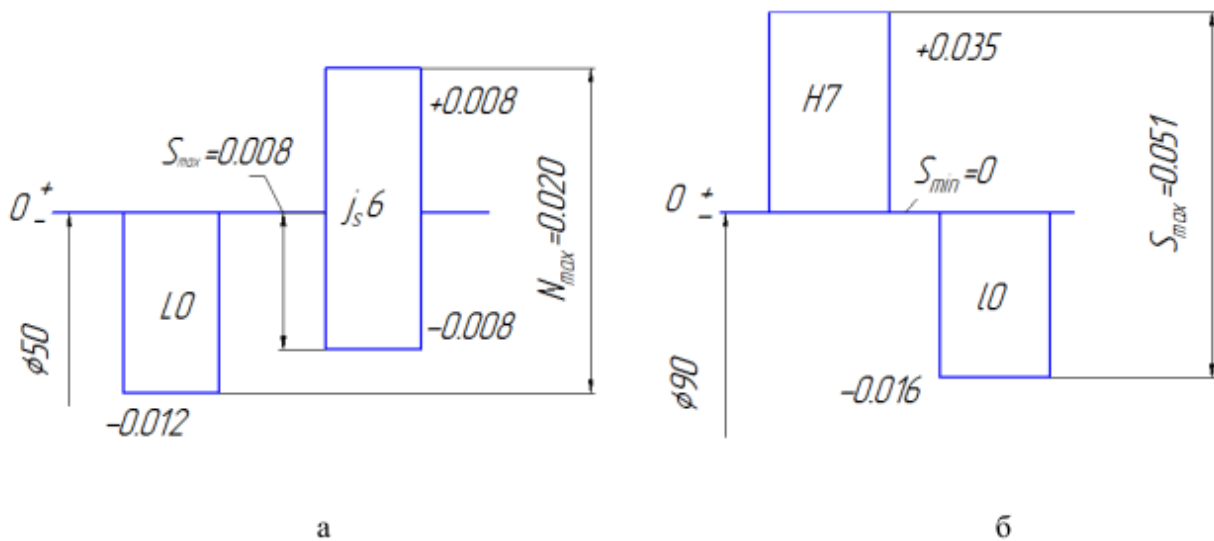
Схеми розташування полів допусків підшипникових посадок: а – внутрішнього кільця підшипника з валом; б – зовнішнього кільця підшипника з отвором корпусу.
